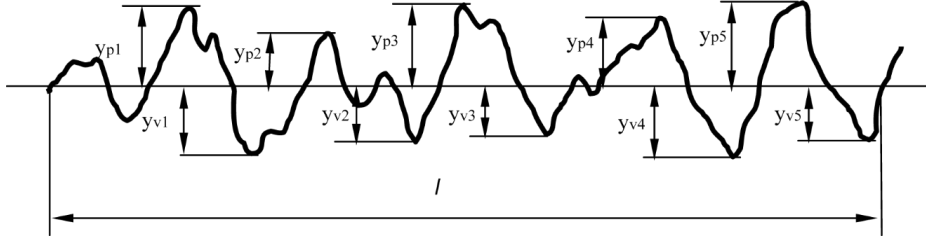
مخطط يبين حساب معدل الخشونة Ra
